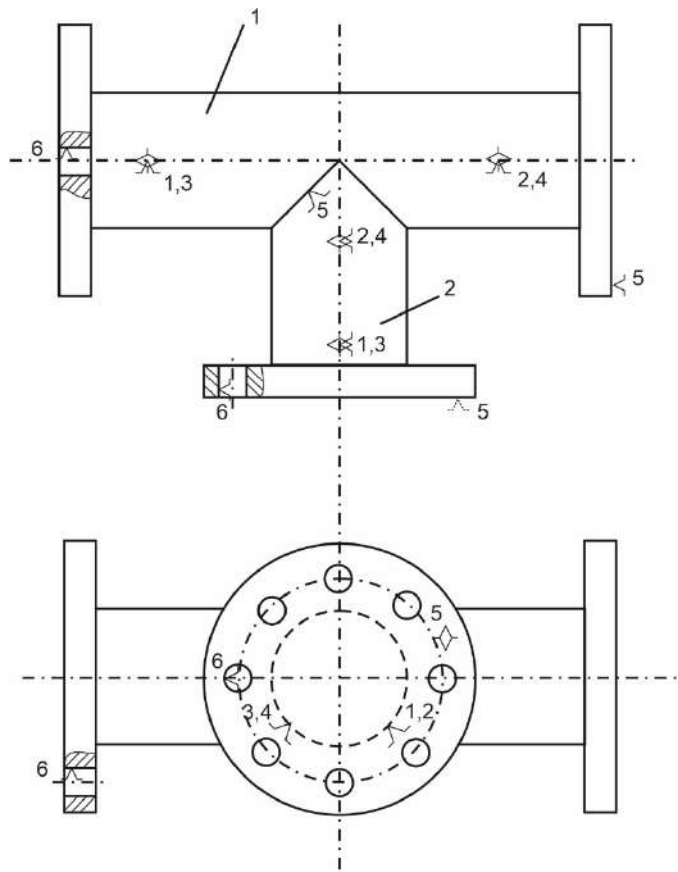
Схема базування деталей патрубка під час зварювання
